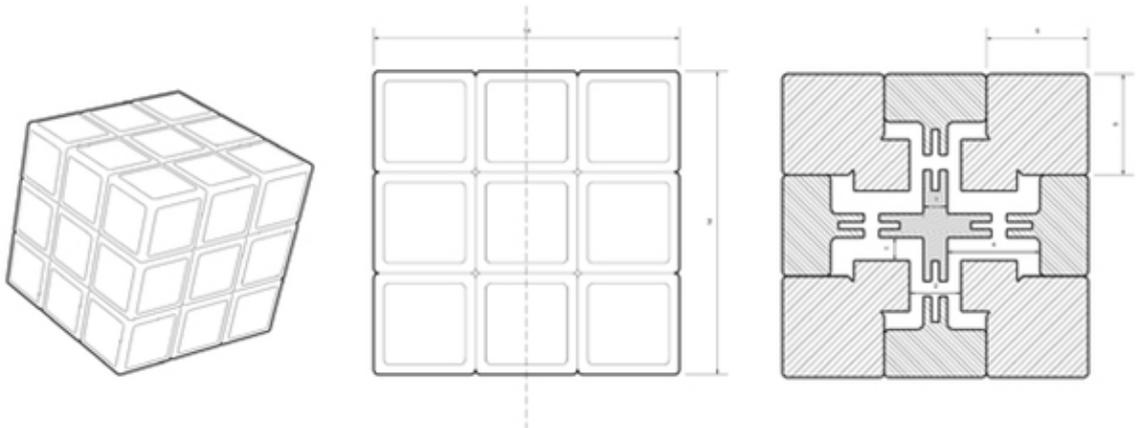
Modelo CAD vista planta cubo de Rubik [13]
